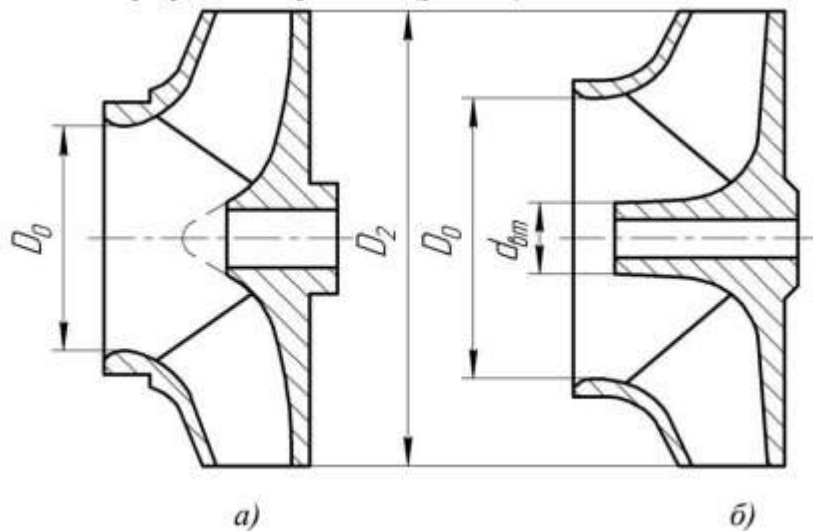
Форма меридіанного перерізу робочого колеса:
